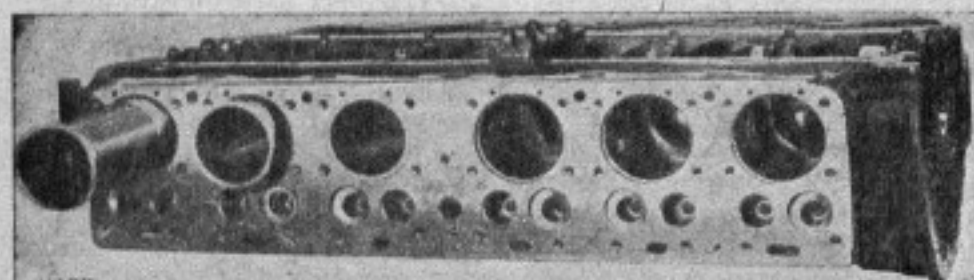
Блок цилиндров двигателя Уайт, модель 10-А
